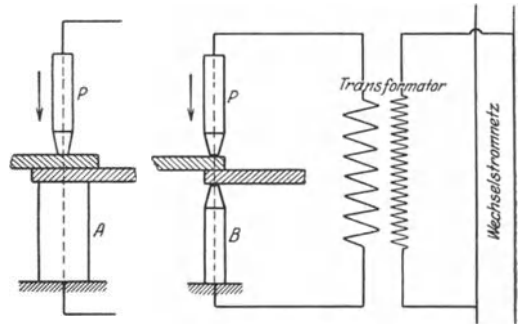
Schema der elektrischen Punktschweißung.
